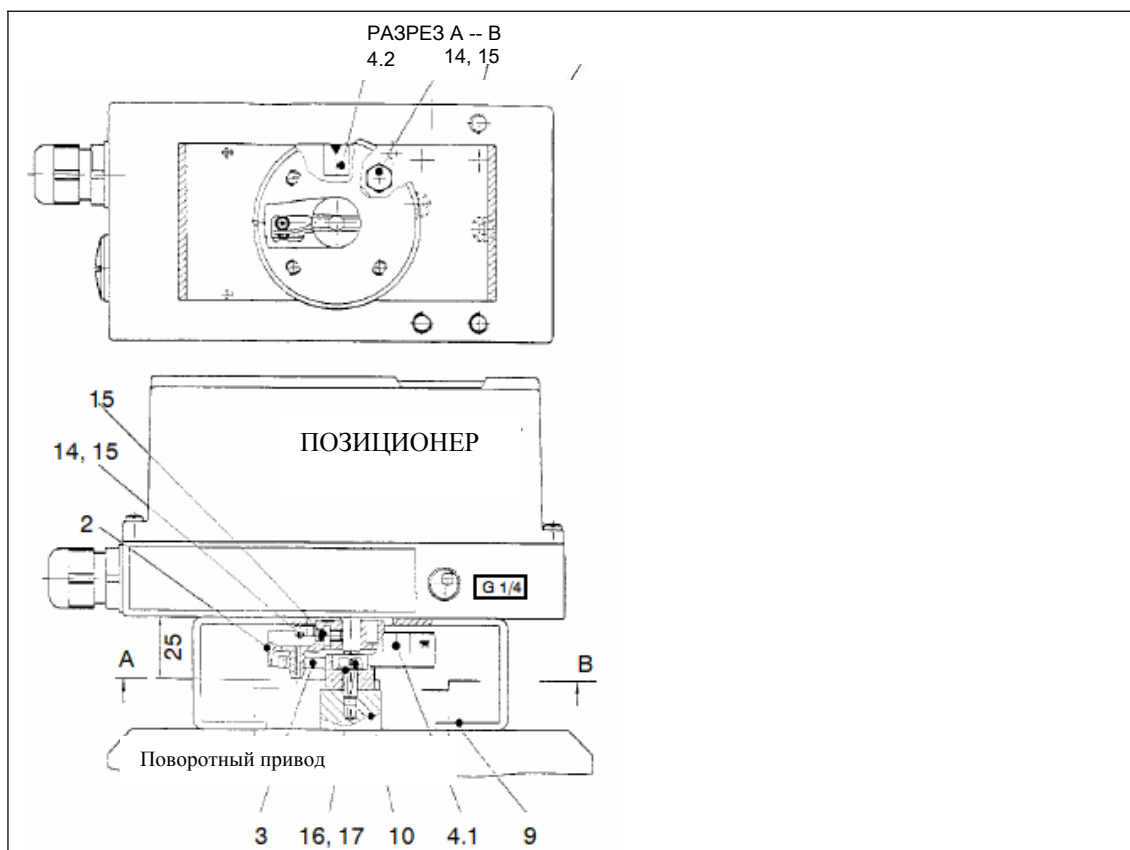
Процесс монтажа для взрывонепроницаемой конструкции (поворотный привод)
